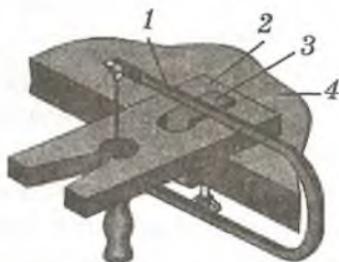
Ручной лобзик и приспособления для выпиливания в собранном виде, готовом для выпиливания: 1 — лобзик, 2 — основание, 3 — струбцина, 4 — крышка стола (верстака)
